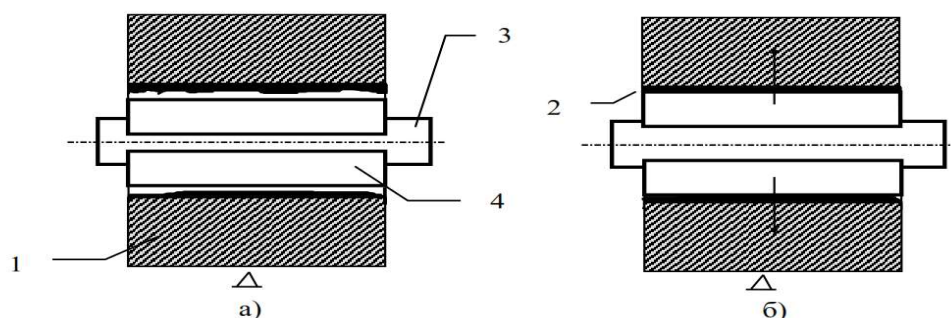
Способ формования полимерного покрытия в отверстии корпусной детали
